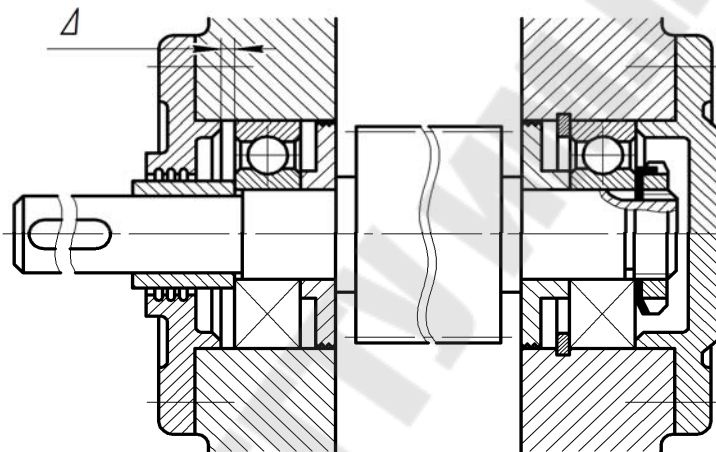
Подшипниковый узел с «плавающим» левым подшипником
